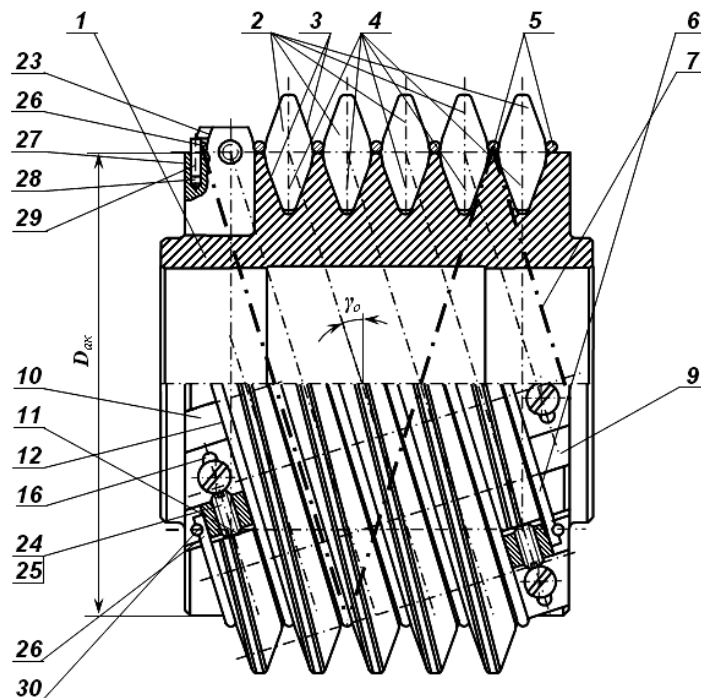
Збірна черв'ячна фреза з пружинним кріпленням ріжучих пластин і клинових вставок між витками її корпусу
